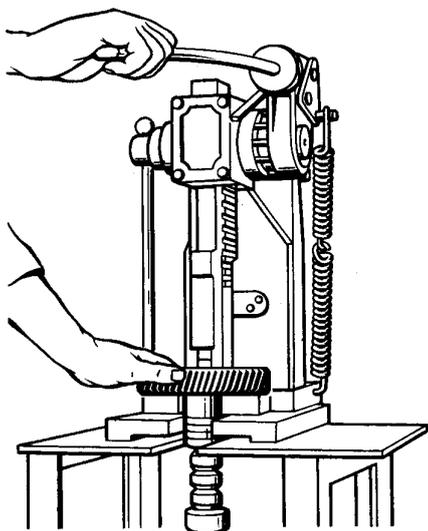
Демонтаж шестерни распределительного вала с помощью прессы
